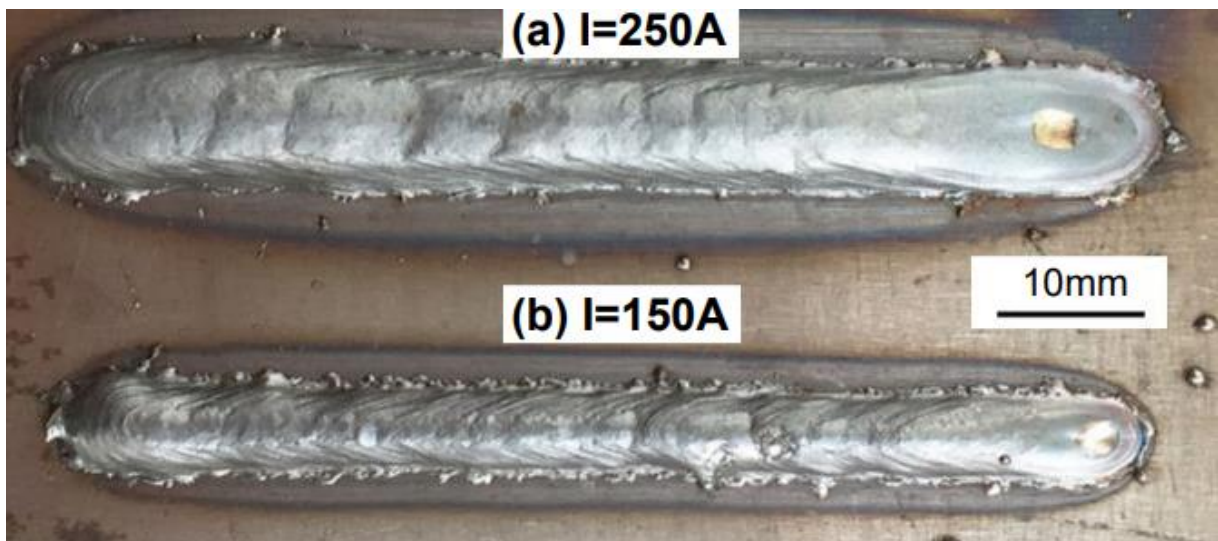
Cordões de solda fabricado com (a) corrente de 250A e (b) 150 A.
